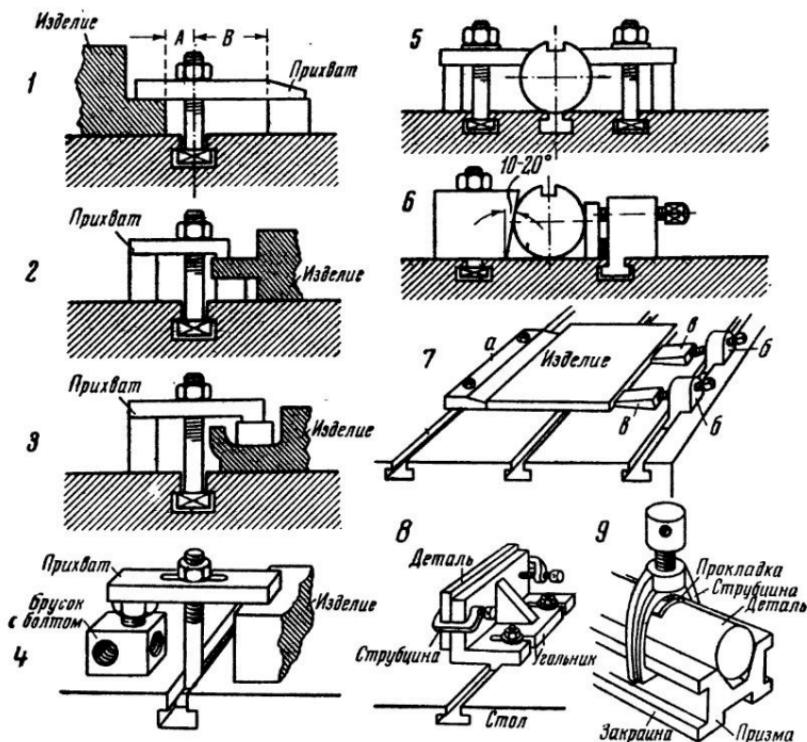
Крепление деталей различной формы на строгальном станке: 1—5 — крепление прихватами; 6 — крепление упорными колодками; 7 — комбинированное крепление (а — упорная планка, б — прижимные колодки, в — упорные клинья); 8 — крепление к угольнику; 9 — крепление к призме.
